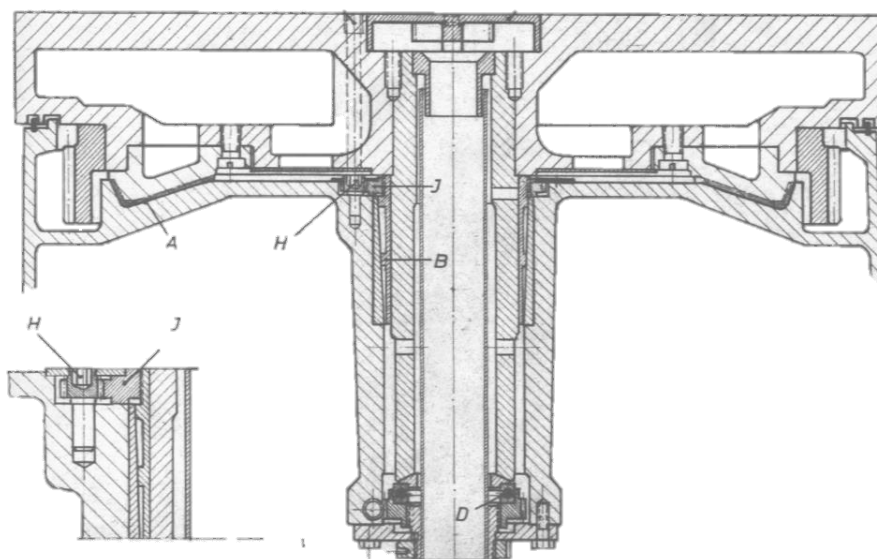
Plan du plateau du tour (diamètre extérieur 2m)
